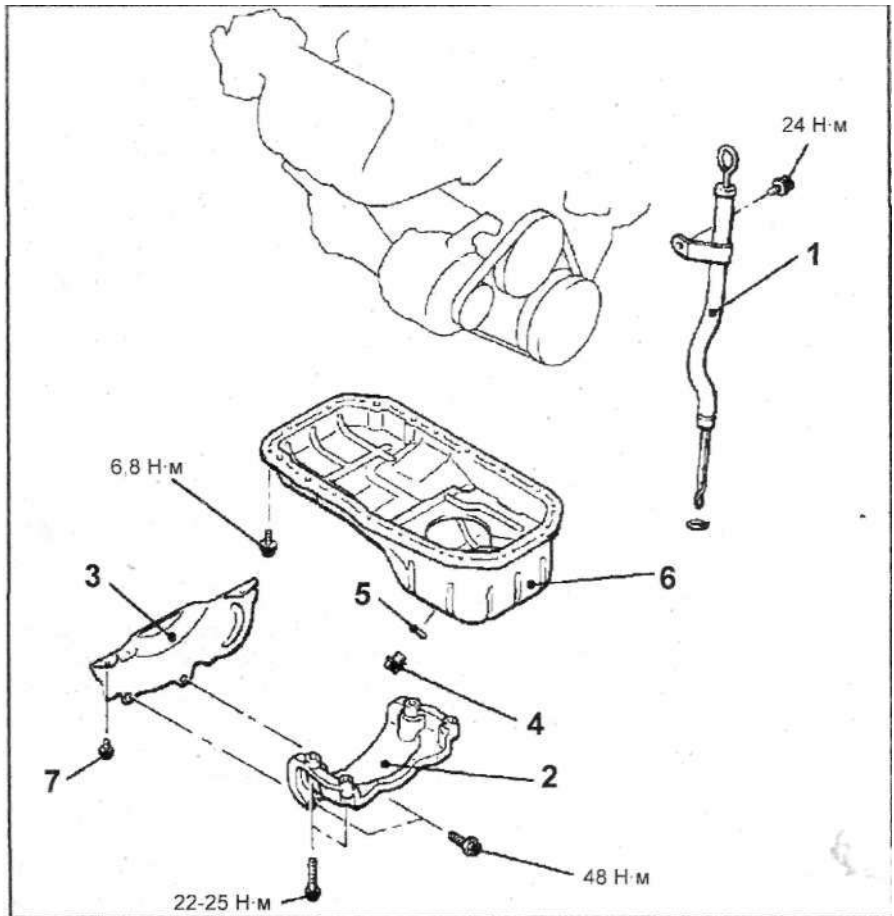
Масляный поддон: 1 - направляющая трубка указателя уровня моторного масла; 2 - опора коробки передач; 3 - крышка картера сцепления; 4 - пробка слива моторного масла, 39 Н·м; 5 - прокладка пробки слива моторного масла; 6 - масляный поддон; 7 - болт с шайбой, 8,8 Н·м (фланцевый болт, 9,8 Н·м)
